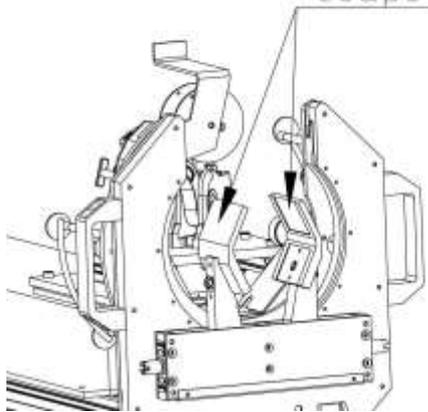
Расположение зажимов сварочной головки
